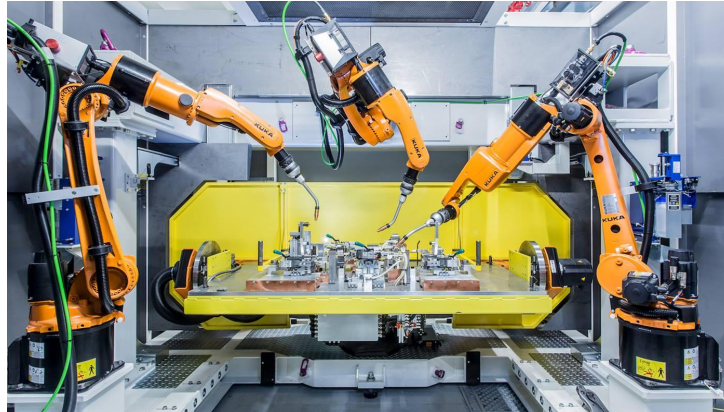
Robots Kuka de 6 grados de libertad realizando el soldado por puntos del chasis de un vehículo.(Fuente: [Soldadura por puntos /KUKA](#))
